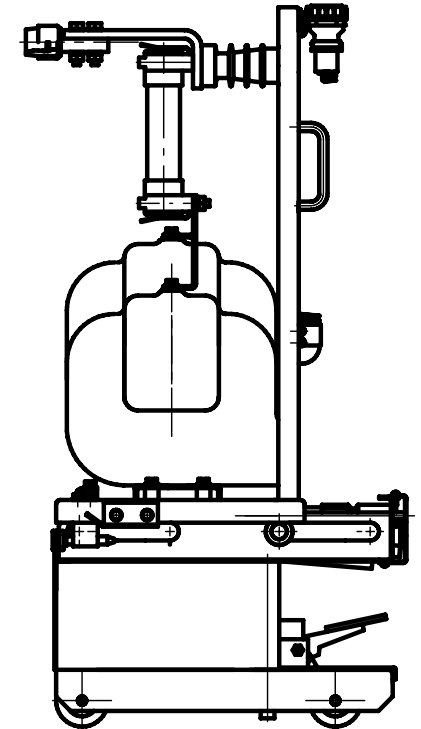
Габаритные и присоединительные размеры выкатных элементов.
